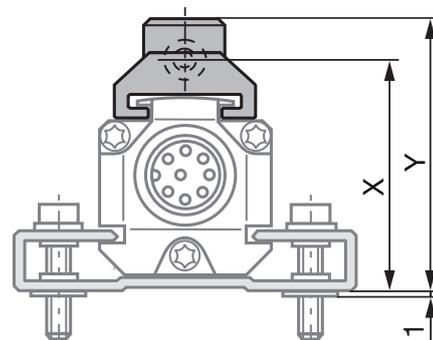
Maße und Abstände mit Positionsgewerber BTL5-M/N-2814-1S
